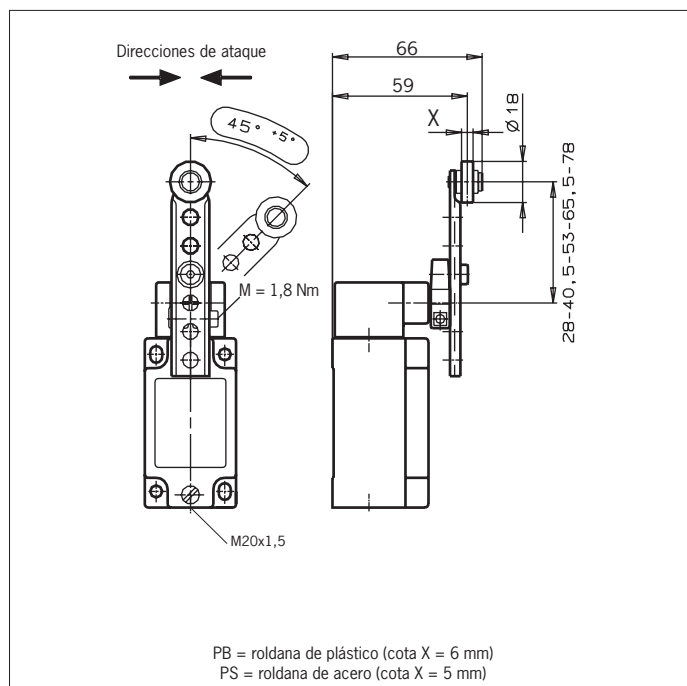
Plano de dimensiones NZ1P.. con entrada de cable
